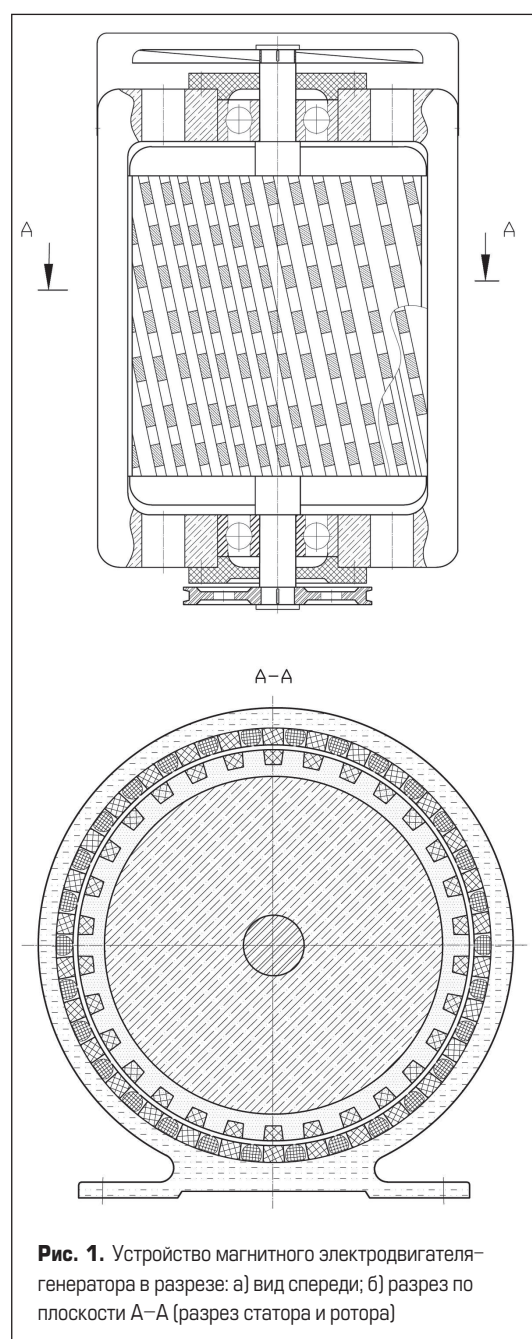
Устройство магнитного электродвигателя-генератора в разрезе: а) вид спереди; б) разрез по плоскости А-А (разрез статора и ротора)
